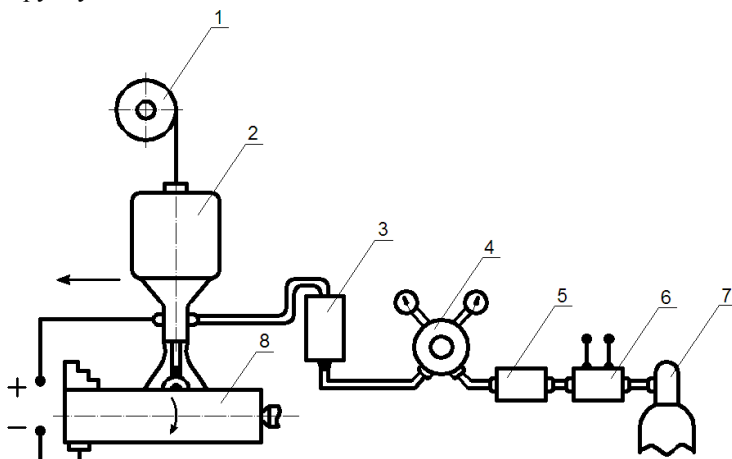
Схема установки для дуговой наплавки в углекислом газе:
